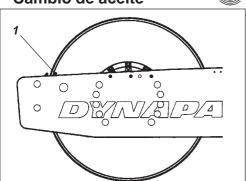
Lado izquierdo del rodillo 1. Espiga indicadora
